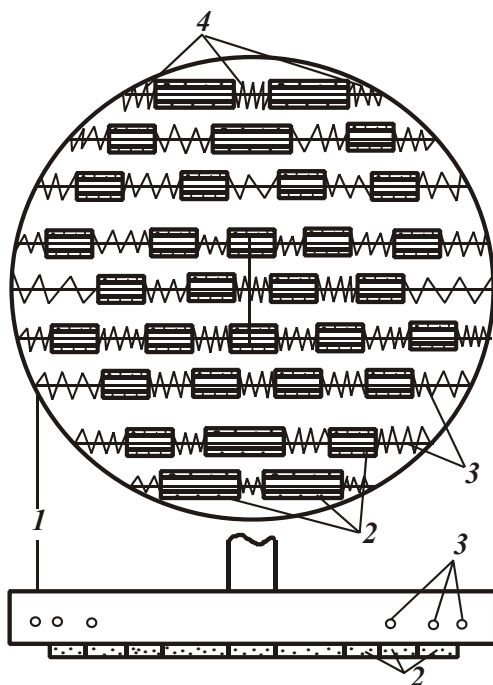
Инструмент для совместной обкатки и шлифования: 1 – корпус; 2 – круг-ролик; 3 – ось, на которой вращается круг; 4 – пружины.
